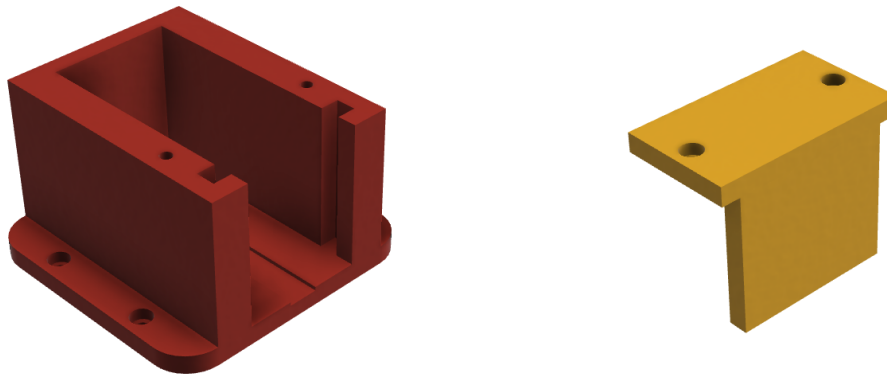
Base para el servomotor a) parte inferior (izquierda), b) parte superior (derecha).
